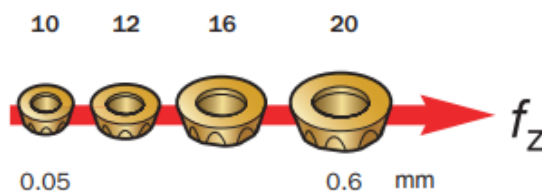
Різальні пластини до торцевої фрези CoroMill 300
